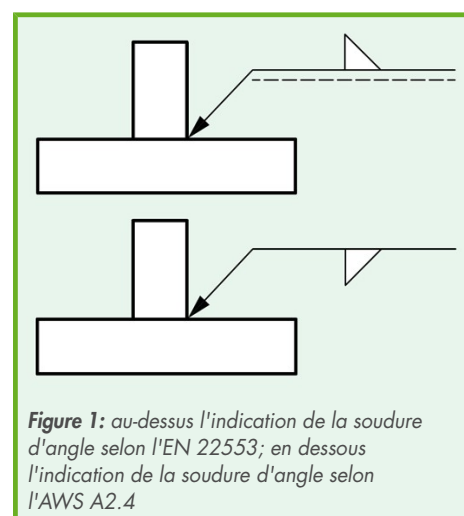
au-dessus l'indication de la soudure d'angle selon l'EN 22553; en dessous l'indication de la soudure d'angle selon l'AWS A2.4
